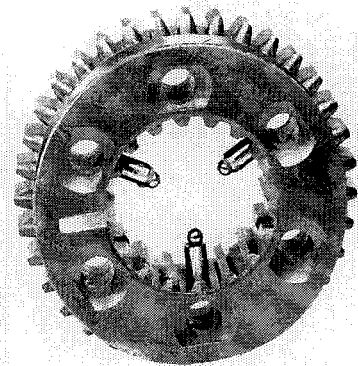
Mit Fett auf den Bolzen befestigte Kugeln
